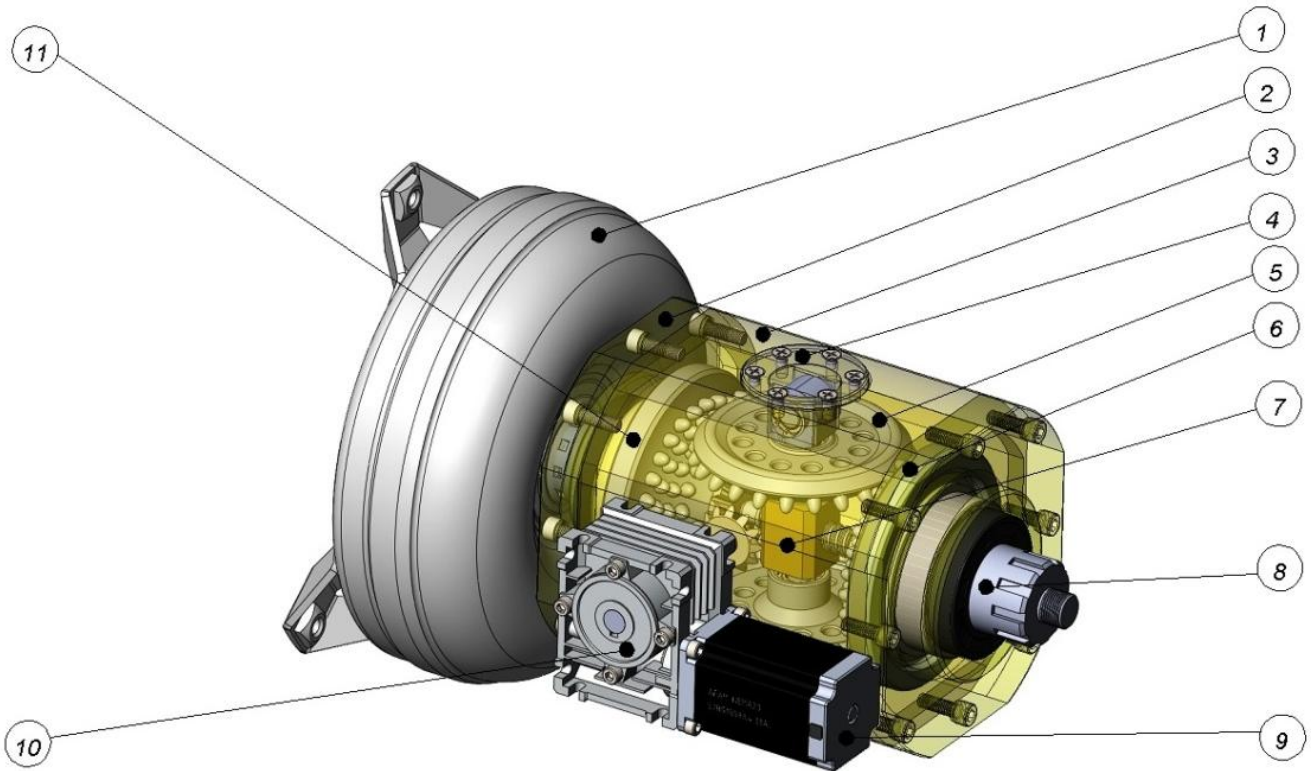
Загальна будова зубчатої варіаторної трансмісії: 1 – гідротрансформатор; 2 – передня кришка; 3 – корпус; 4 – механізм коливання сателіту; 5 – сателіт; 6 – задня кришка; 7 – механізм зміни передаточного числа; 8 – ведений вал; 9 – кроковий двигун; 10 – черв'ячний редуктор; 11 – тороїдне зубчасте колесо із ведучим валом
